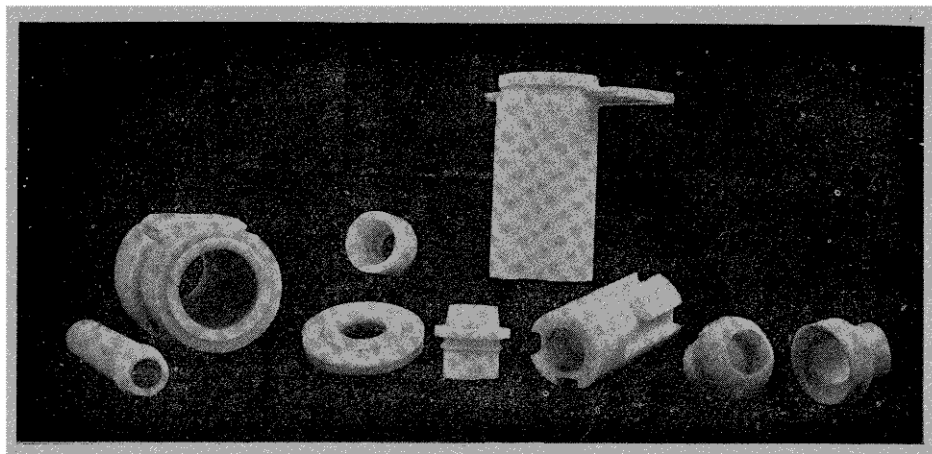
Vue de quelques pièces usinées de précision en silice fondue.
